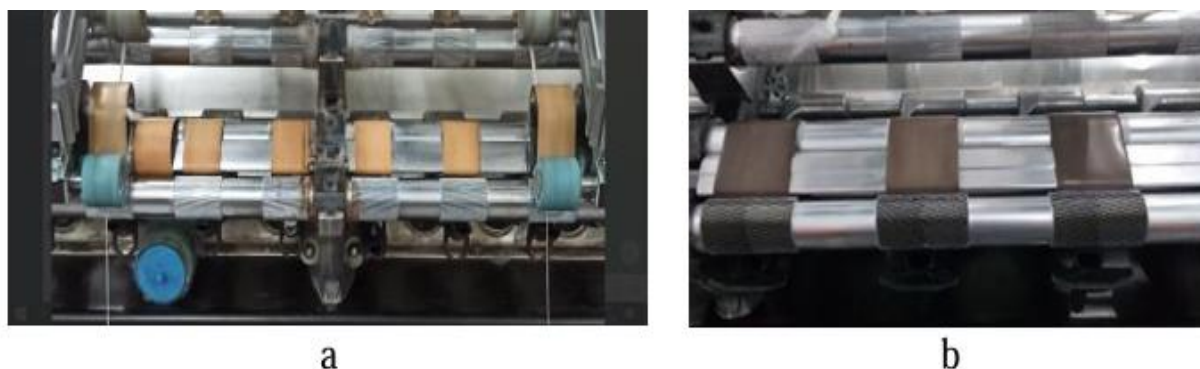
Цилиндры с выпускной рифлей вытяжного прибора кольцепрядильной машины. а) Стандартный рифлёный цилиндр, б) цилиндр с косоугольной рифлёный рекомендуемой новой конструкции
